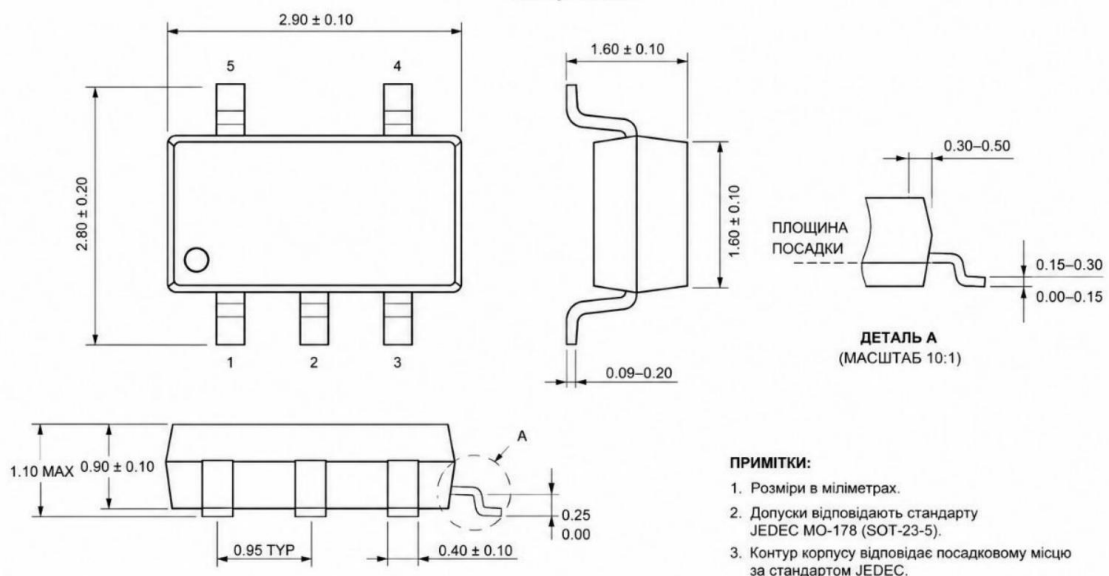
Зовнішній вигляд і розміри корпусу лінійного стабілізатора напруги ADP150AUJZ-3.3-R7
